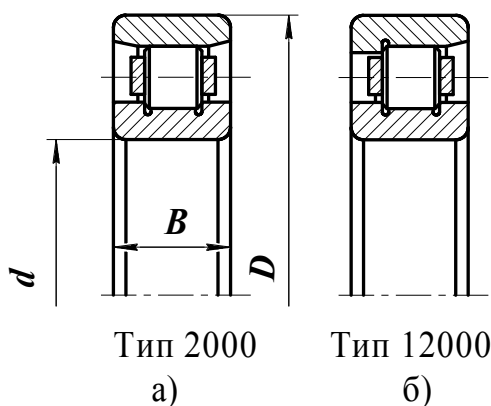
Підшипники радіальні з короткими циліндричними роликами
